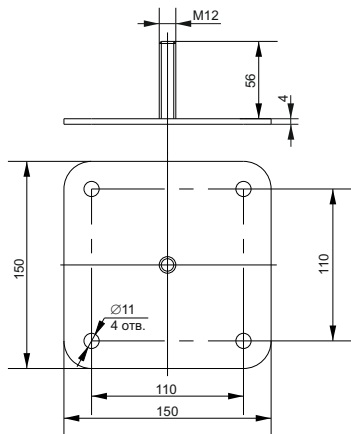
Габаритные размеры держателя / Figure 1 – Overall dimensions of the holder / 1 сурет – ұстатқыштың жалпы өлшемдері
